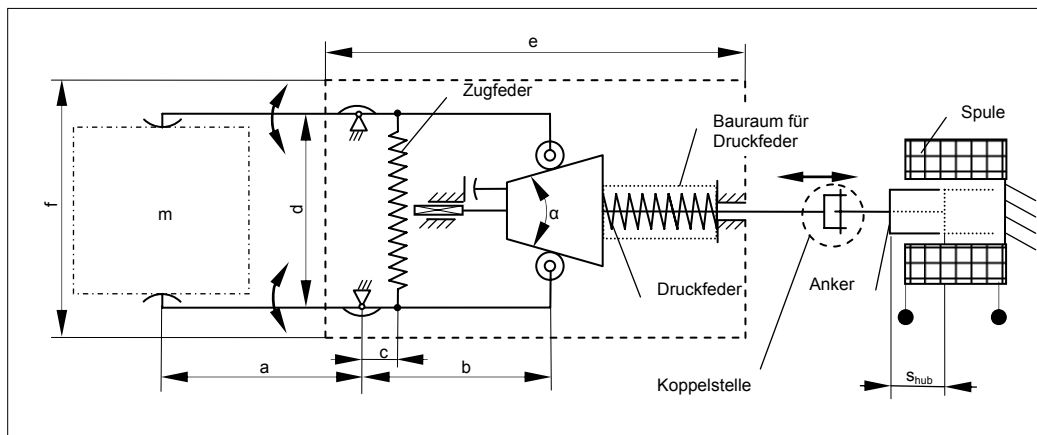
Greifer in Position „ZU“, (Draufsicht)
